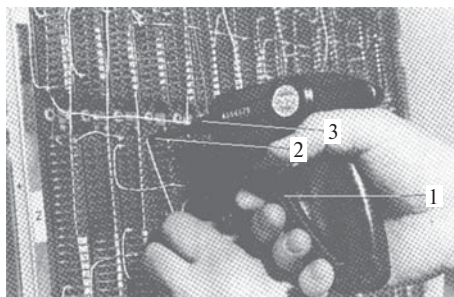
Инструмент для накрутки в руках оператора: 1 — курок инструмента; 2 — оправка; 3 - шпindelь
